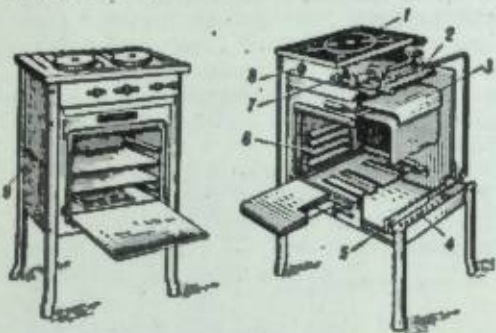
Газовая плита с 2 конфорочными горелками; слева — общий вид; справа — разрез; 1 — рабочий стол; 2 — поддон; 3 — конфорка; 4 — дно духового шкафа; 5 — горелка духового шкафа; 6 — направляющая противня; 7 — распределительный шток; 8 — ручка крана; 9 — отверстие для выхода продуктов сгорания из духового шкафа.
